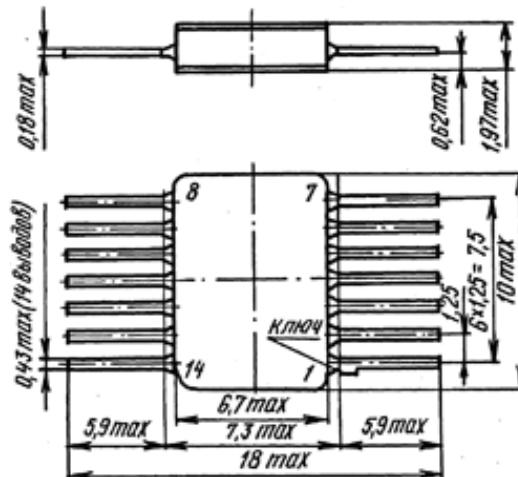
Габаритные чертежи корпусов 401.14-4 и 401.14-5М
